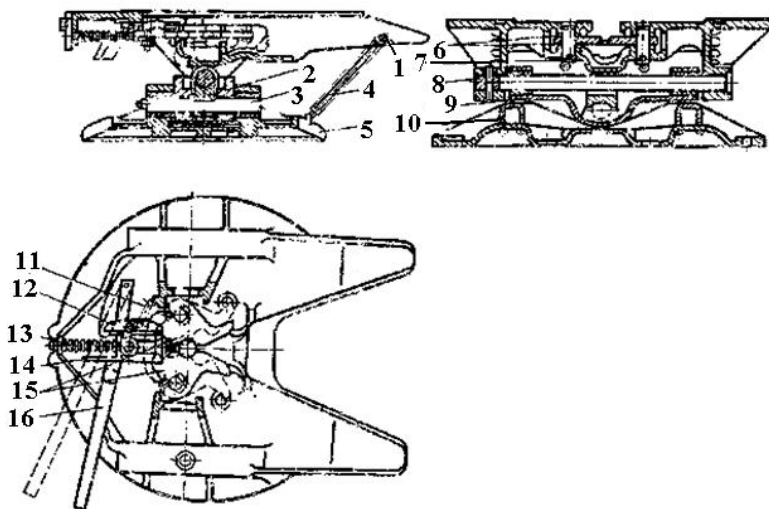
Зчіпний сидельний пристрій [9]:
